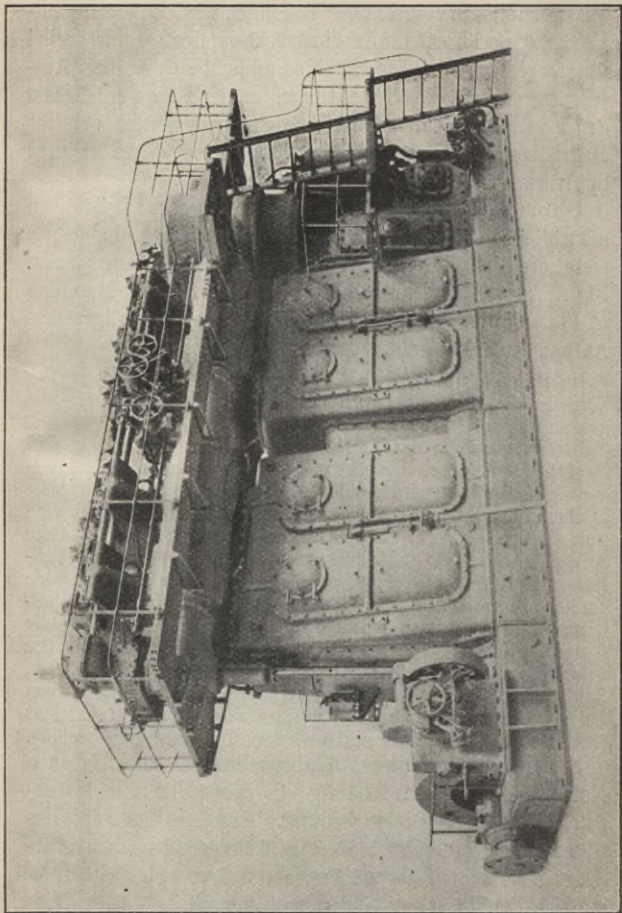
Umsteuerbare Vierzylinder-Zweitaktsschiffsdieselmotoren von Gebr. Sulzer, $N_i = 1700$ PSI, $n = 100$ Umdr./Min.
